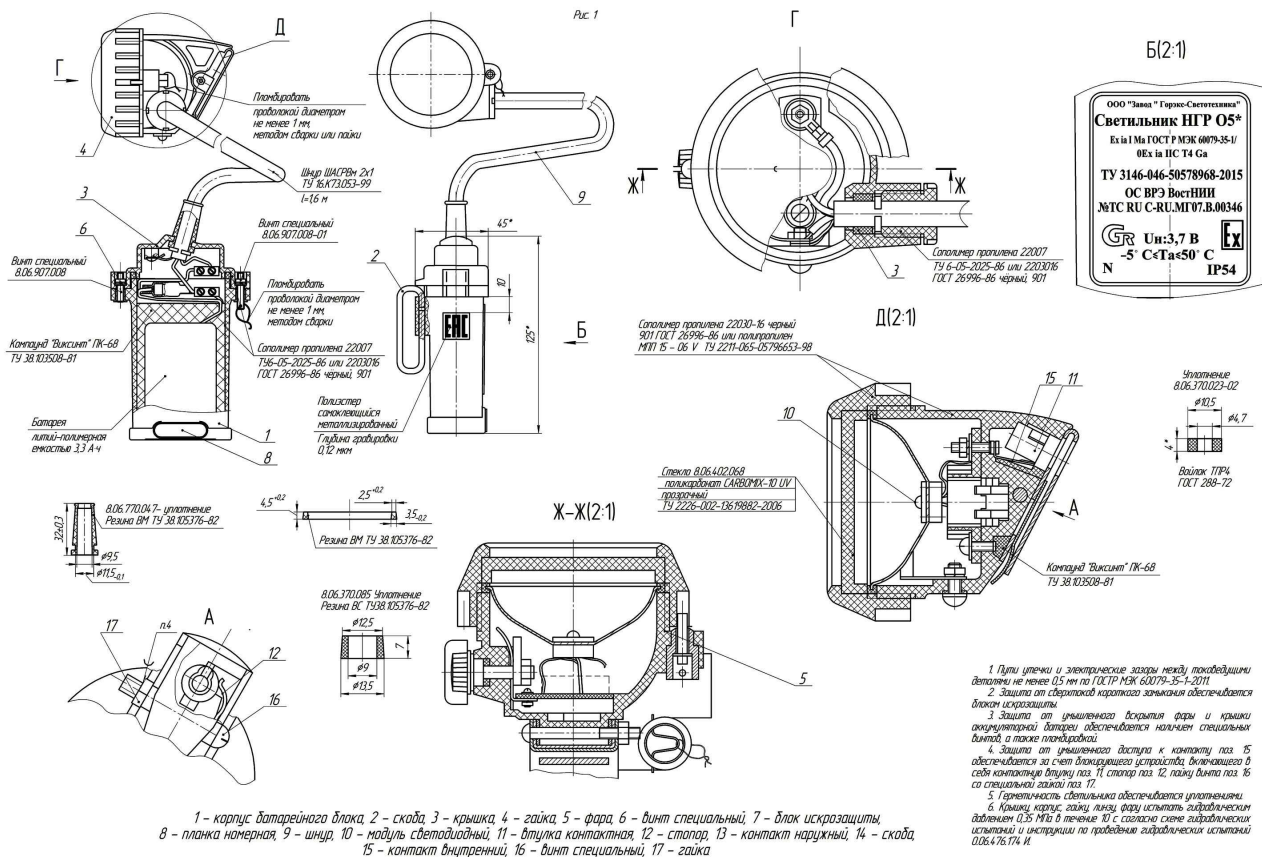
Общий вид и чертеж взрывозащиты светильника
